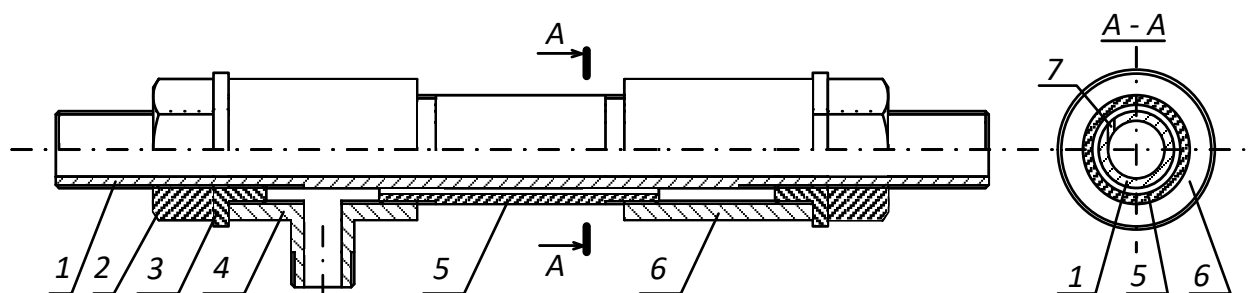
Конструкция образца смесителя: 1 – смесительная трубка; 2 – контргайка; 3 – переходник; 4 - тройник; 5 –сгон; 6 – муфта; 7 – отверстие
